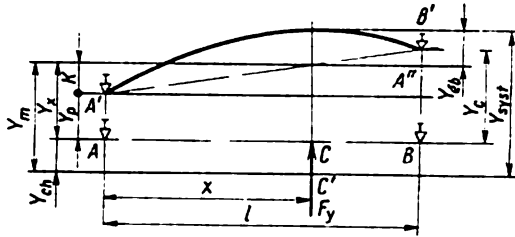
Illustration du calcul des refoulements d'un système élastique machine-pièce
